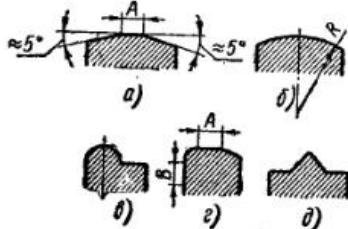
Профили роликов для обкатывания наружных поверхностей:
